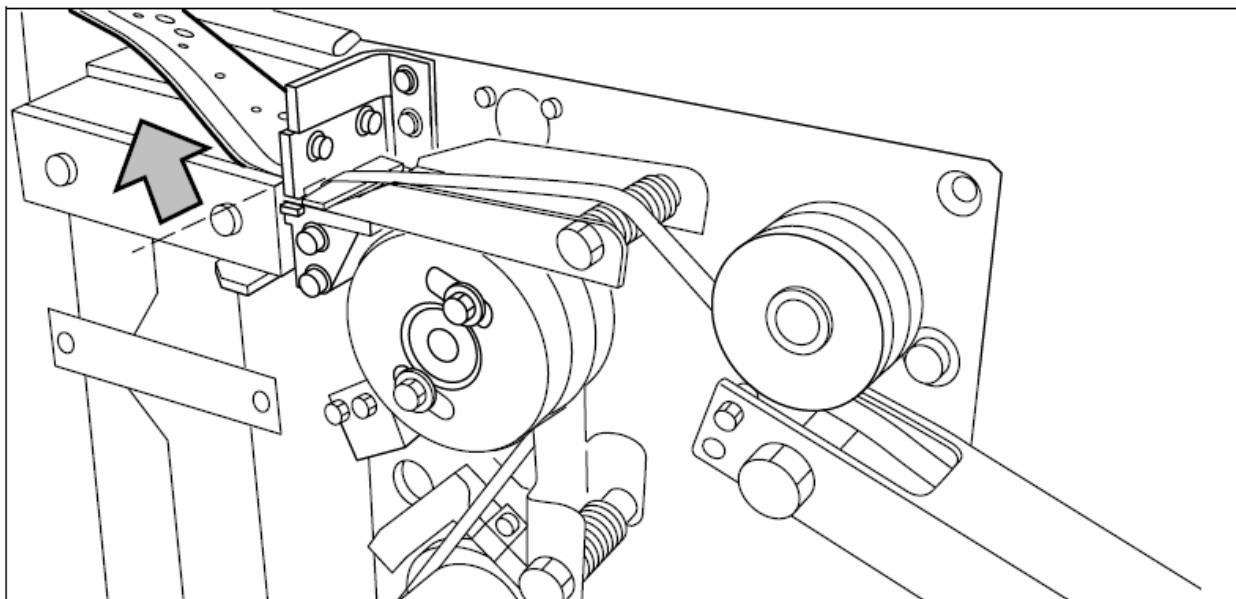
Обрезка самоклеящейся ленты с помощью верхнего ножа
